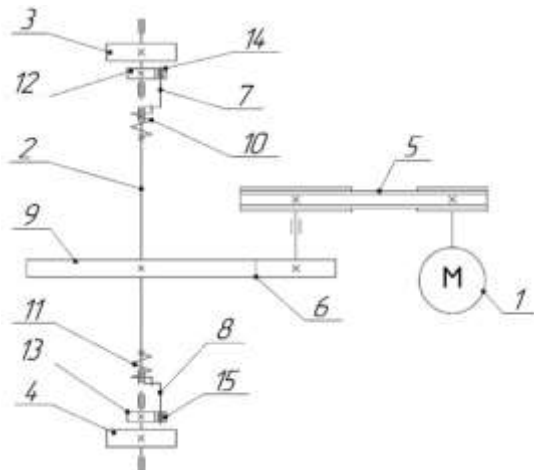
Кінематична схема привода круглов'язальної машини з ПЗДН з пружинами кручення: 1 – електродвигун; 2 – приводний вал; 3, 4 – шестерні; 5 – клинопасова передача; 6 – зубчаста передача; 7, 8 – ведучі напівмуфти; 9 – зубчасте колесо; 10, 11 пружини кручення; 12, 13 – ведені напівмуфти (сонячні шестерні); 14, 15 – шестерні сателіти
